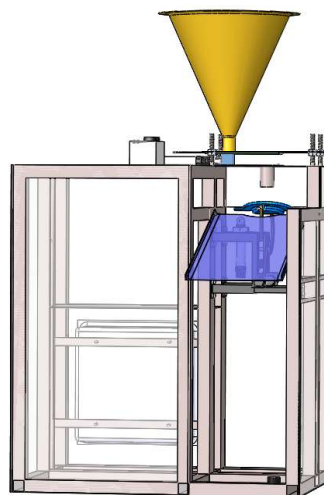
Vista isométrica del ensamble del mecanismo de corte y sellado.
